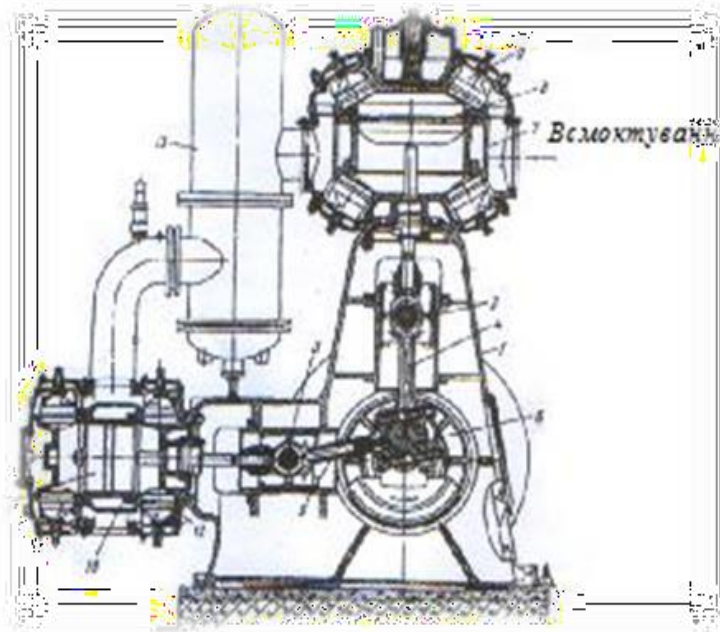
Поршневий компресор 305ВІ-30/8
